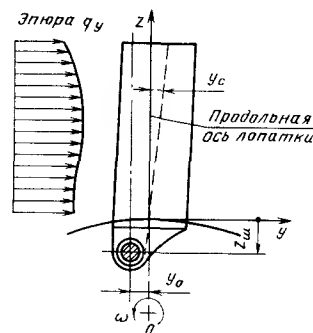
К определению положения шарнира компрессорных лопаток с шарнирным креплением
